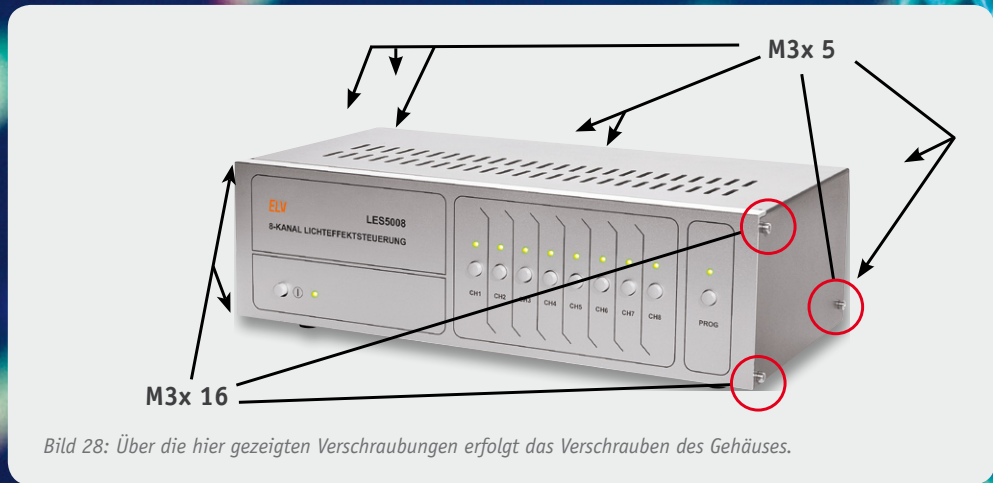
Über die hier gezeigten Verschraubungen erfolgt das Verschrauben des Gehäuses.
